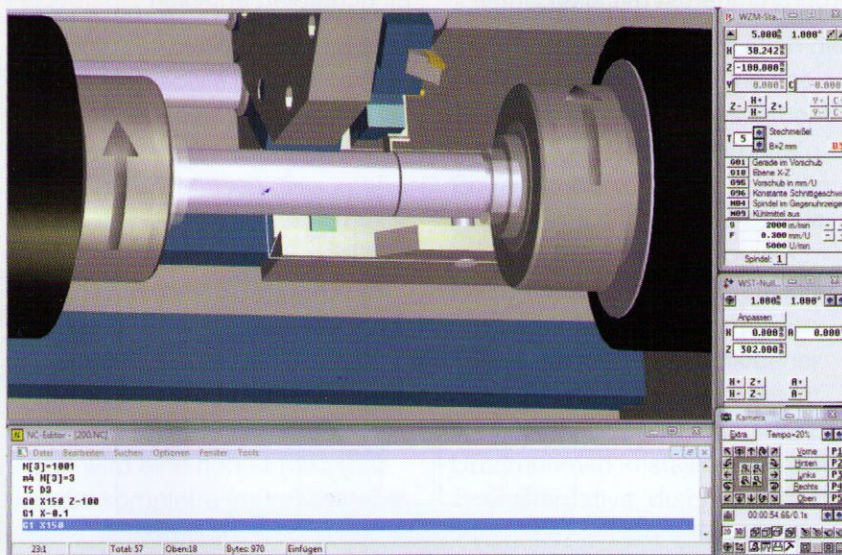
Programmierung von Maschinentypen mit Gegenspindel
